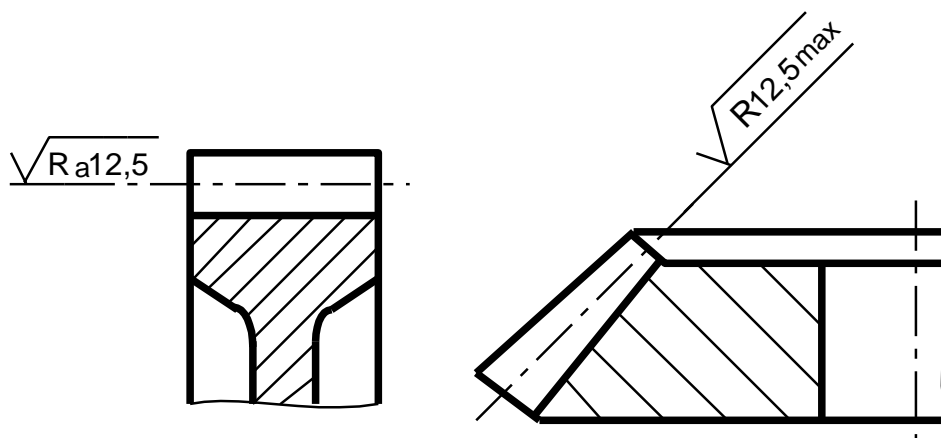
Обозначение шероховатости рабочих поверхностей зубьев зубчатых колес и эвольвентных шлицев
